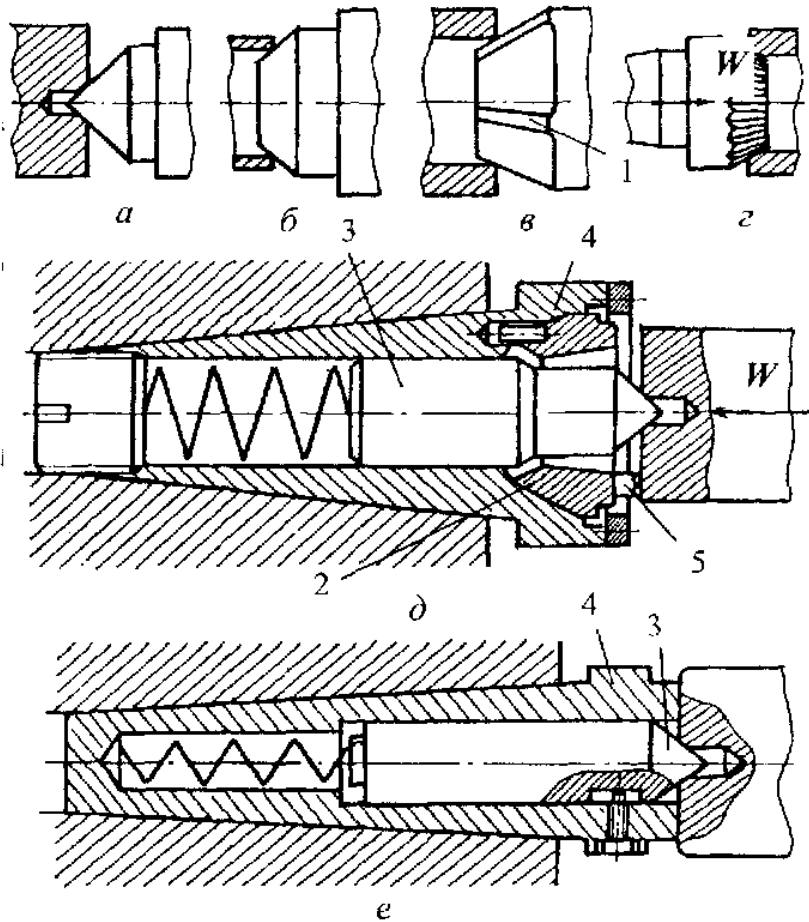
Схеми встановлення заготовок на центрові гнізда та конічні фаски
